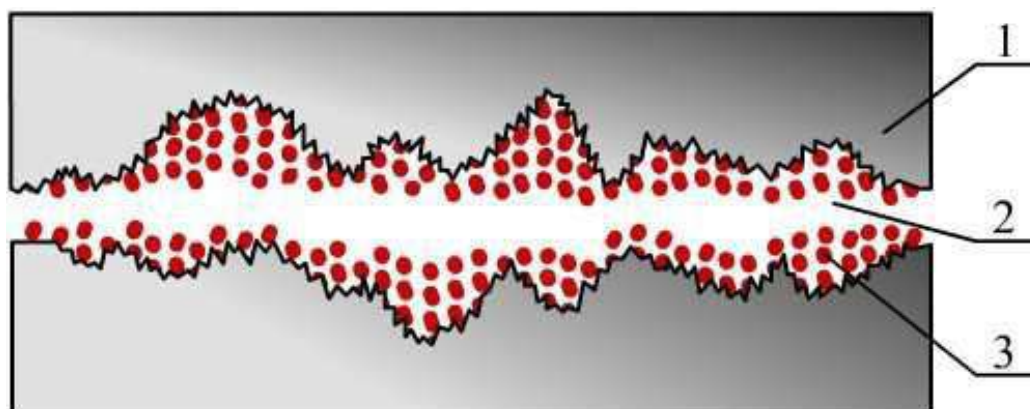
Структура поверхні, відновленої реметалізатором: 1 – металева поверхня деталі; 2 – мастильний матеріал; 3 – «серовита» плівка
